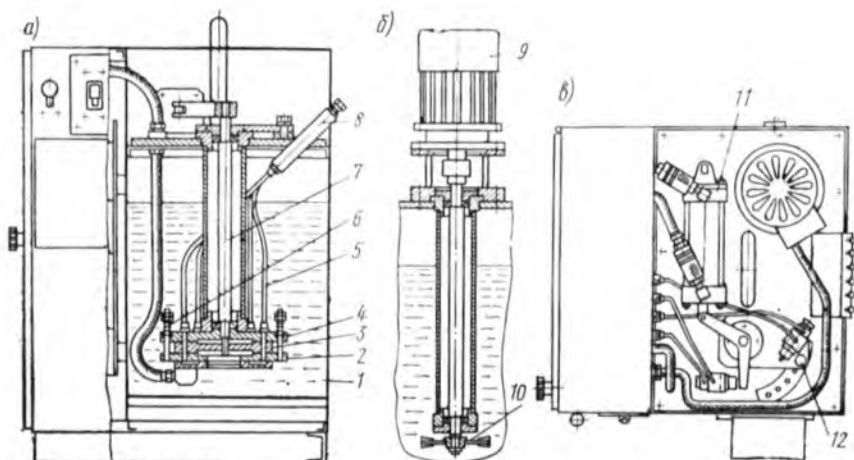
Установка УО-223 для автоматической дозированной смазки штампов:
